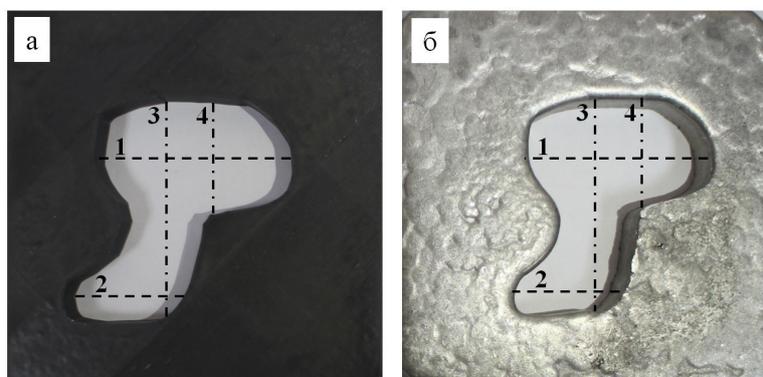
Внешний вид а – пластикового и б – металлического коллиматоров
